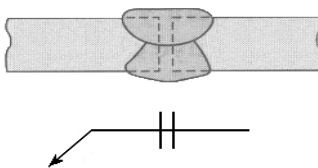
Cuadrada soldadura a tope ambos lados.
